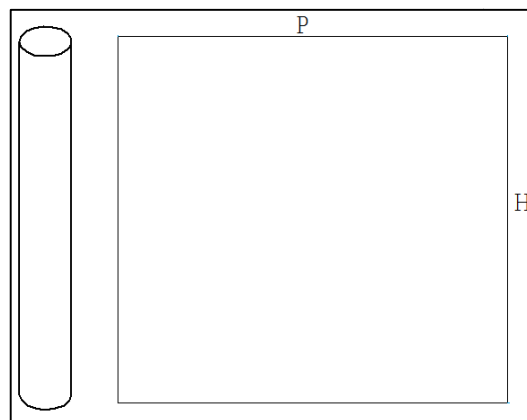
Primer tramo de la chimenea auxiliar. (Elaboración propia)
